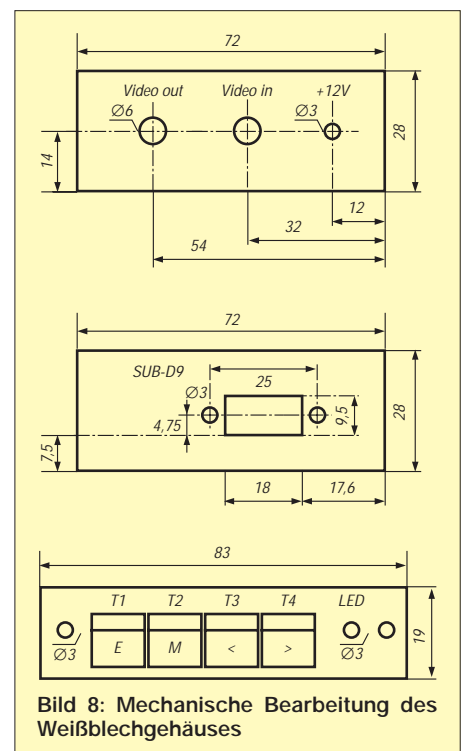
Mechanische Bearbeitung des Weißblechgehäuses
